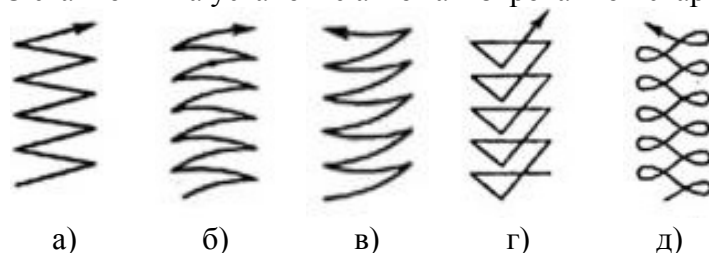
Основные схемы перемещения сварочного электрода при ручной сварке: а – зигзаг; б, в – полумесяцем; г – треугольником; д – восьмёркой
